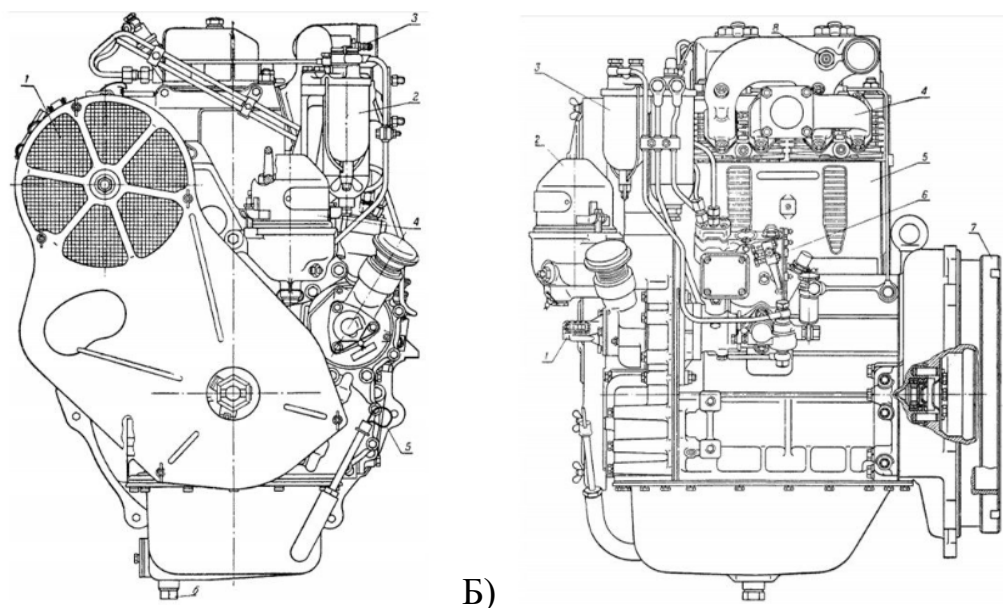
Дизельный двигатель Д-21 (А – вид спереди, Б – вид слева)
